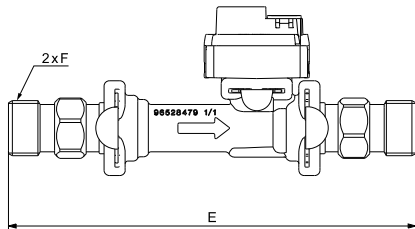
Abmessungen des Sensors MFS 2-20 l/min (mit Adapter)
